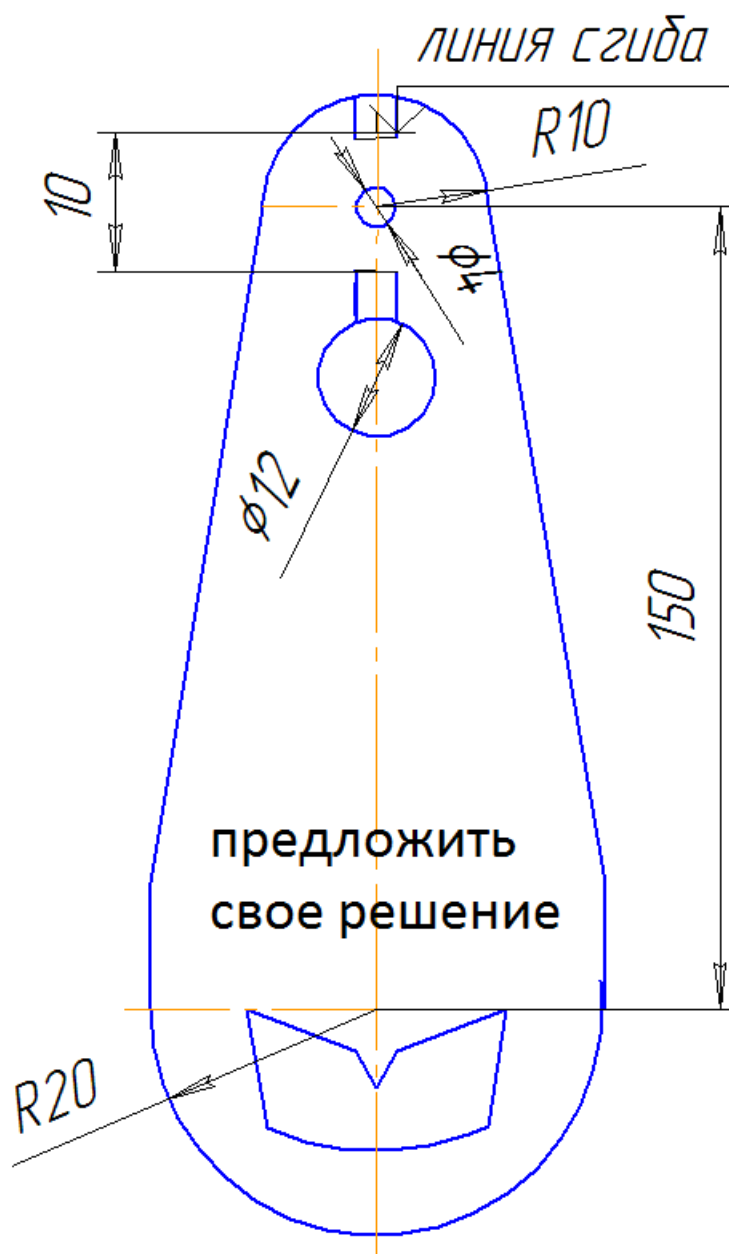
Подвижная «линейка» с оправкой для зеркальца
